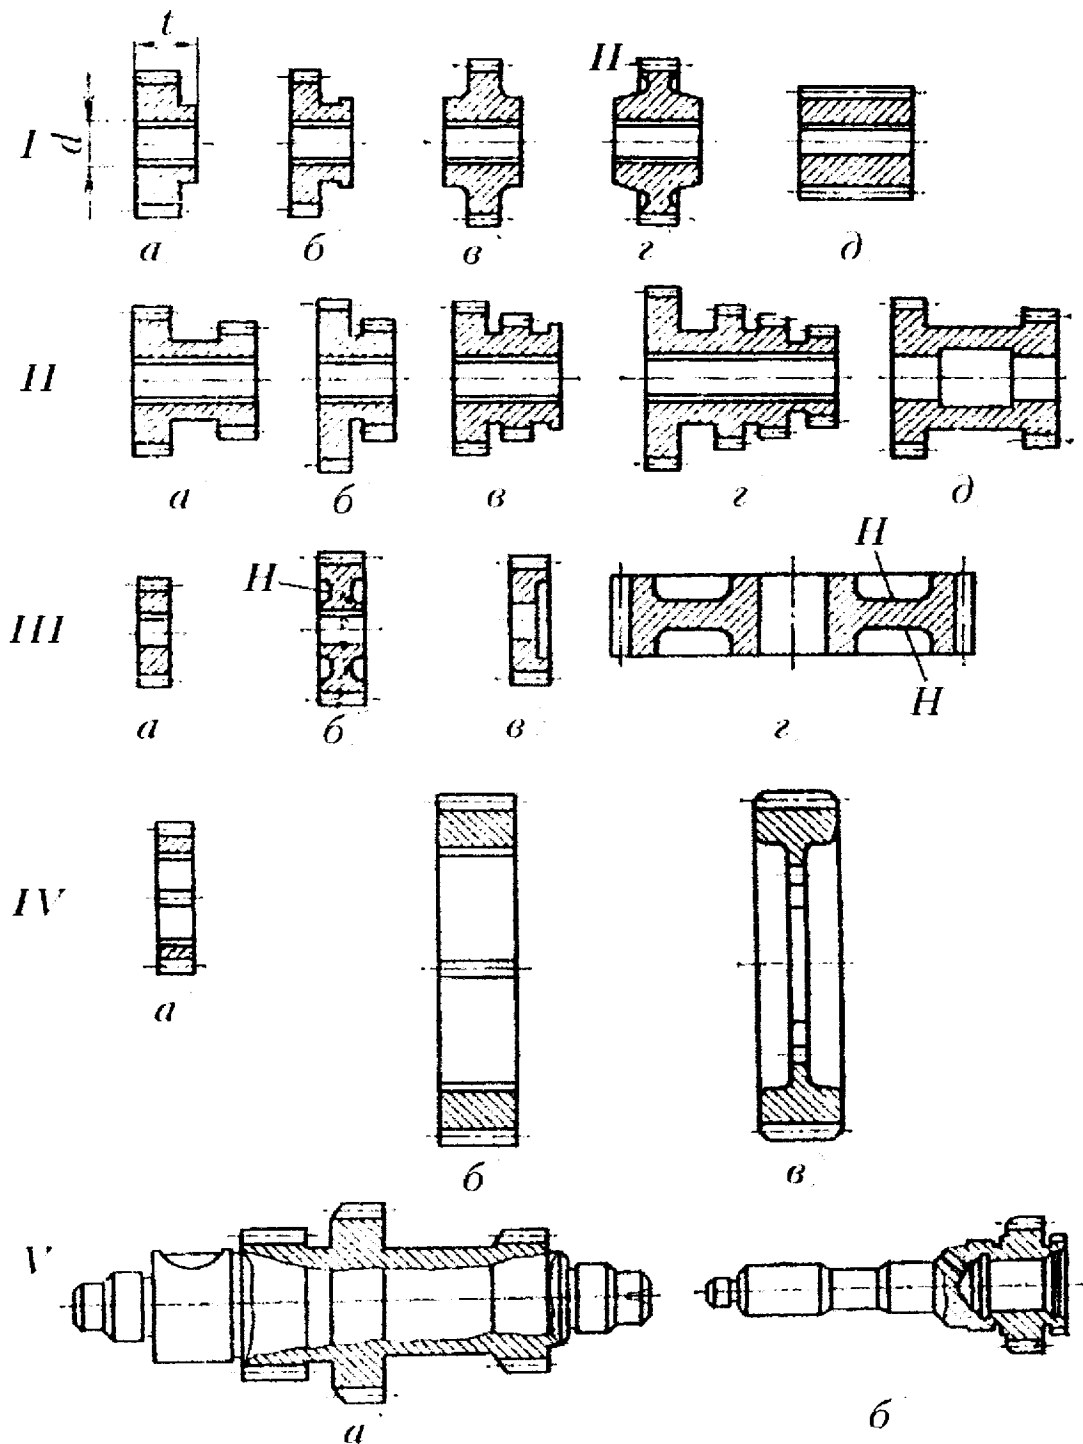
Конструктивные разновидности цилиндрических зубчатых колес
